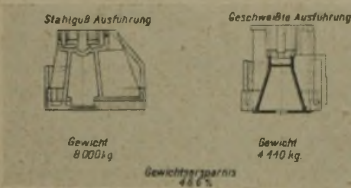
Gewichtsvergleich einer Stahlguß- und Schweißkonstruktion des Gegenrahmens zum Arbeitsrollgang mit Traversenanschlüssen
